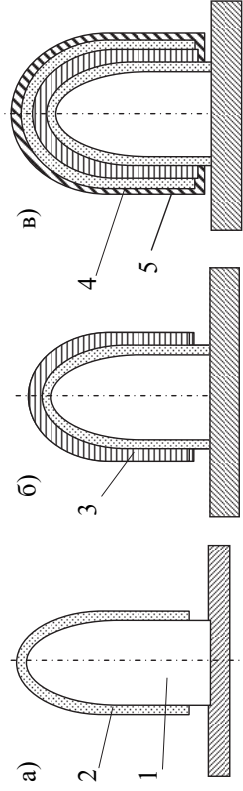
Изготовление обтекателя в три перехода: 1 – болванка; 2 – сотовый заполнитель; 3 – слой внешней обшивки; 4 – цулага
